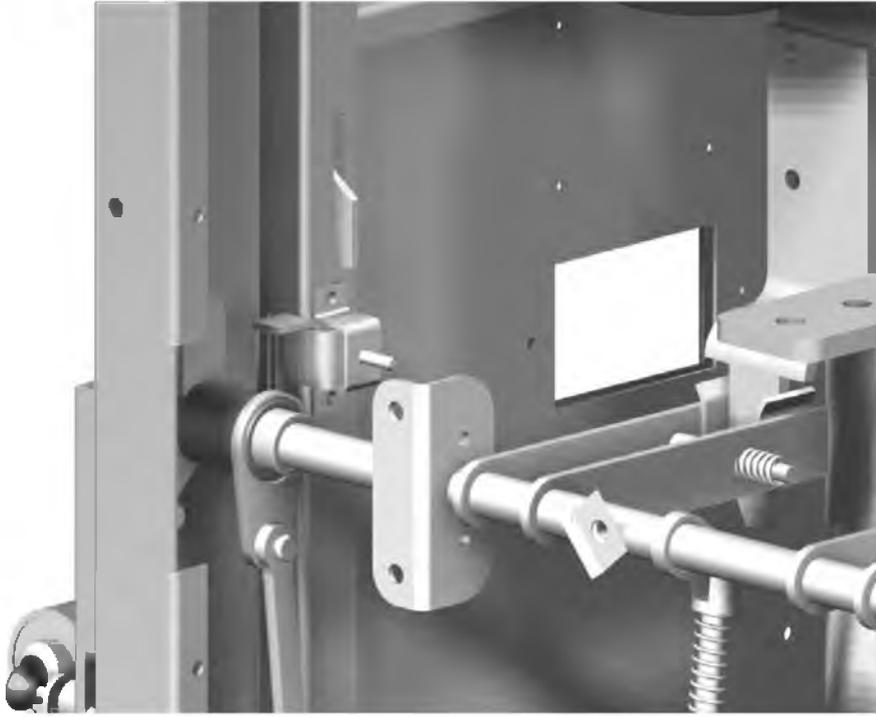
Блокировка двери высоковольтного отсека и заземляющего разъединителя
